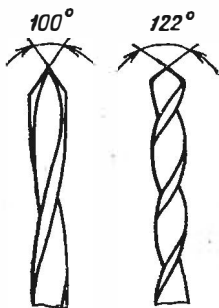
Два типа сверл, используемых для сверления слоистых пластиков.
